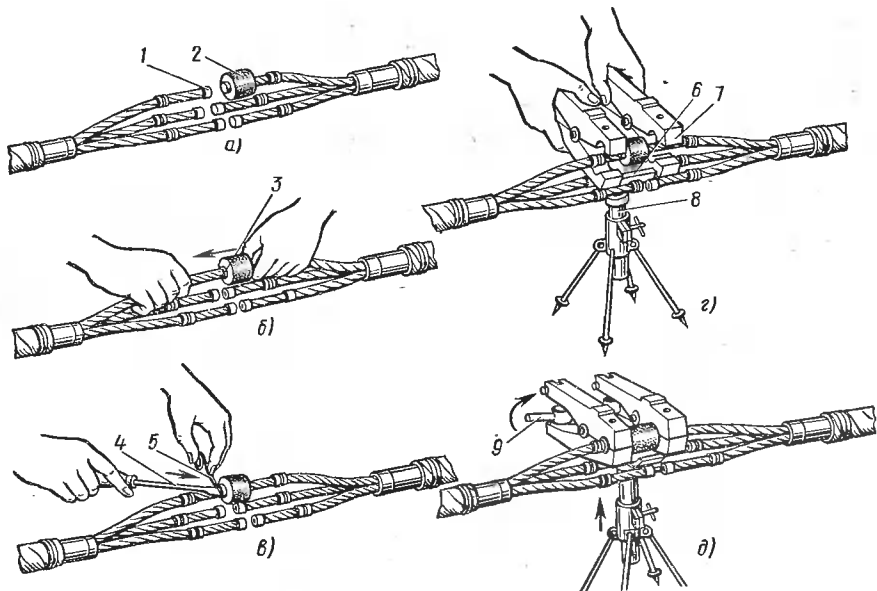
Операции подготовки жил к термитной сварке:
